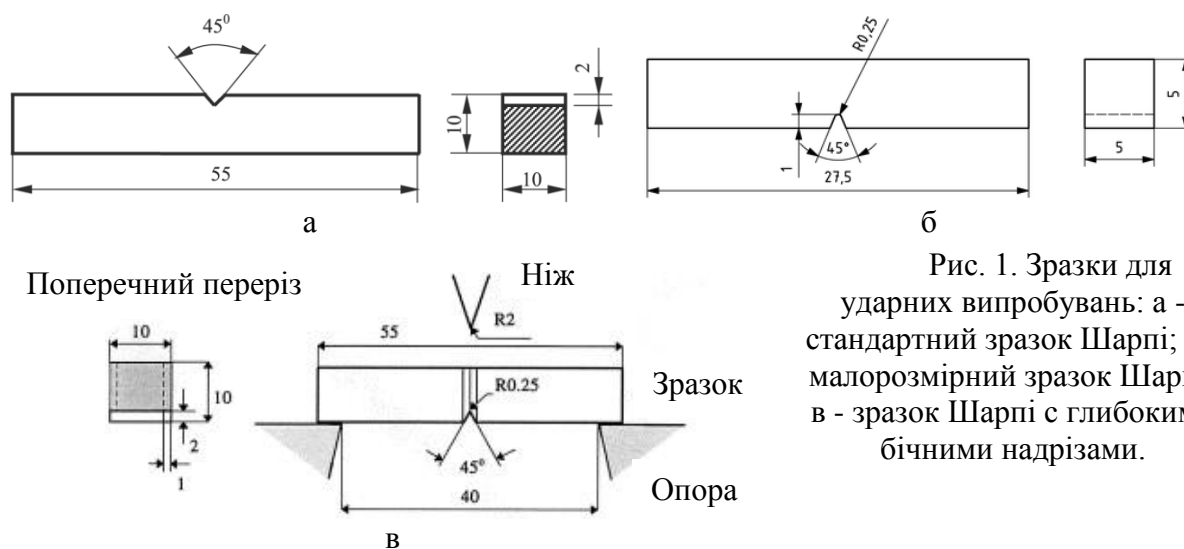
Зразки для ударних випробувань: а - стандартний зразок Шарпі; б - малорозмірний зразок Шарпі; в - зразок Шарпі з глибокими бічними надрізами.
